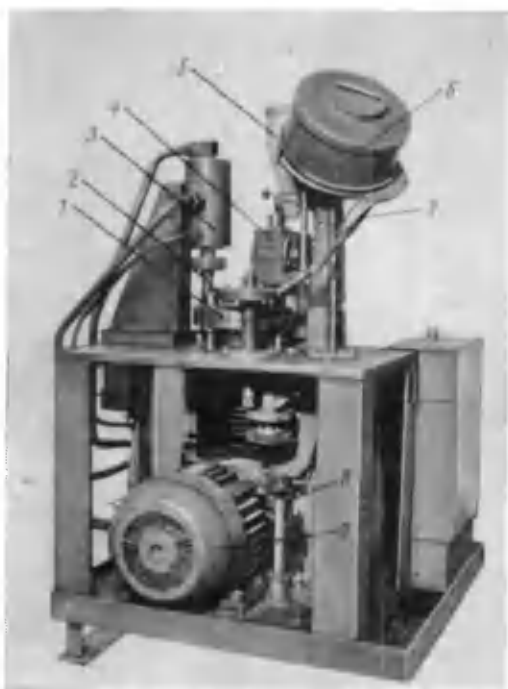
Роторный автомат для запрессовки цинкового порошка в крышки ртутно-цинковых элементов:
